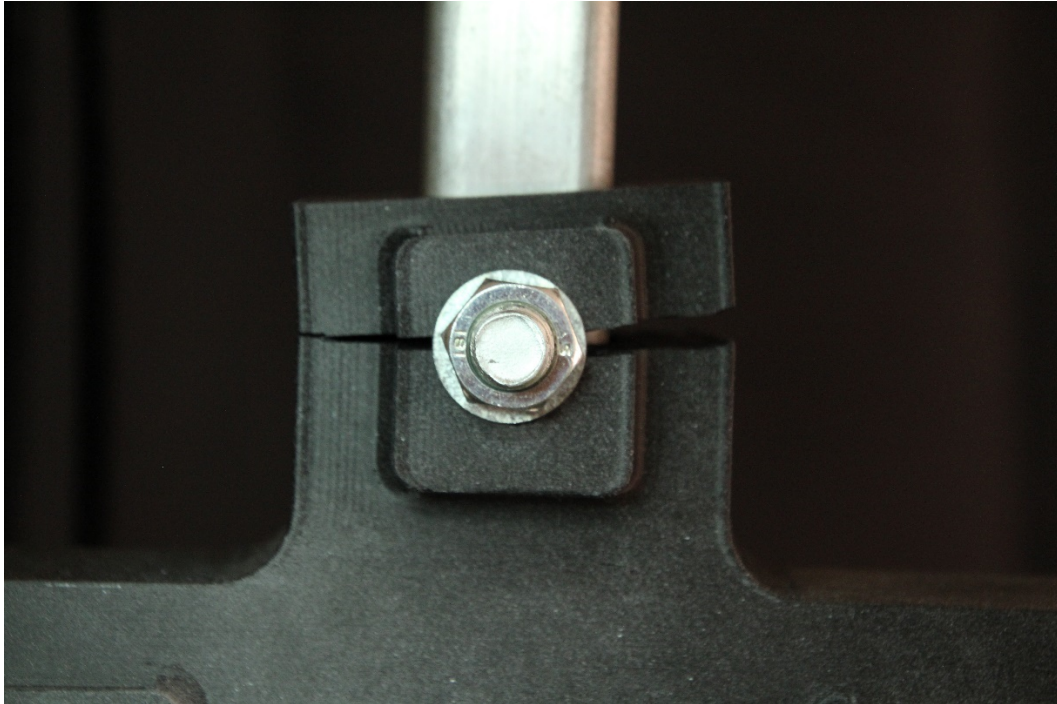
Detalle 1 de rotura del Prototipo 2 a tracción.
